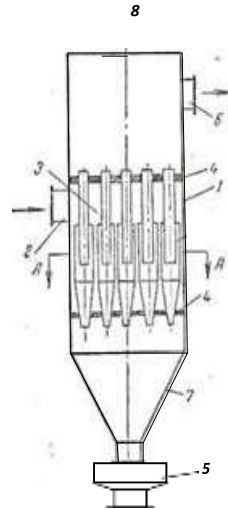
Батареїний циклон: 1 – корпус циклона; 2 – вхідний патрубок; 3 – газорозподільна камера; 4 – трубні решітки; 5 – пилосбірник; 6 – вихідний патрубок для очищеного газу; 7 – конічне днище (бункер), 8 – кришка
